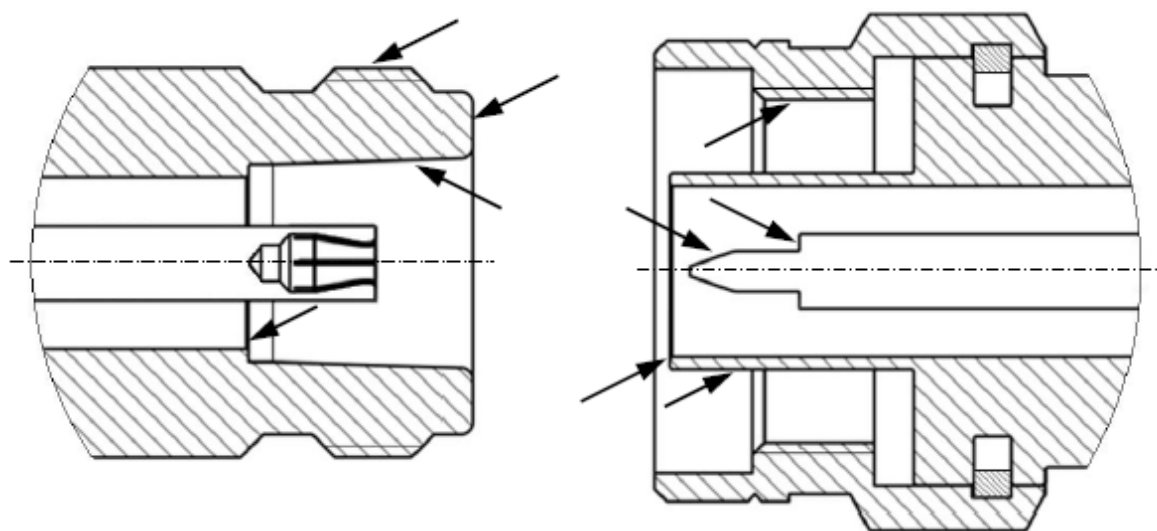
Соединители тип N и III (розетка и вилка)
